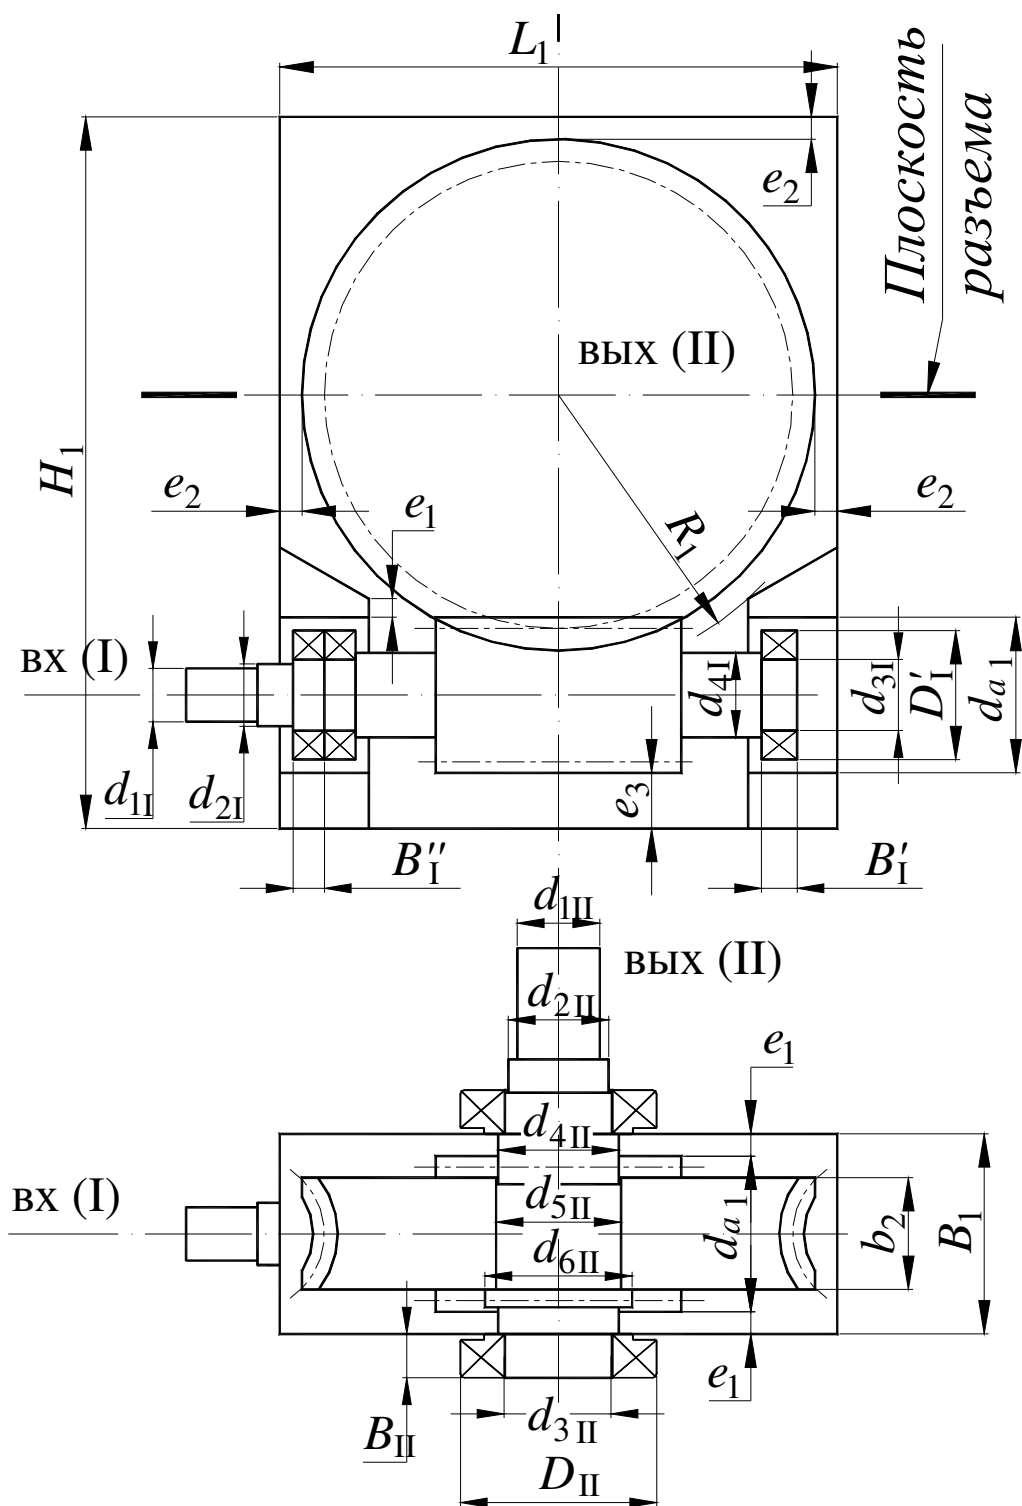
Эскизная компоновка червячного редуктора с нижним расположением червяка
